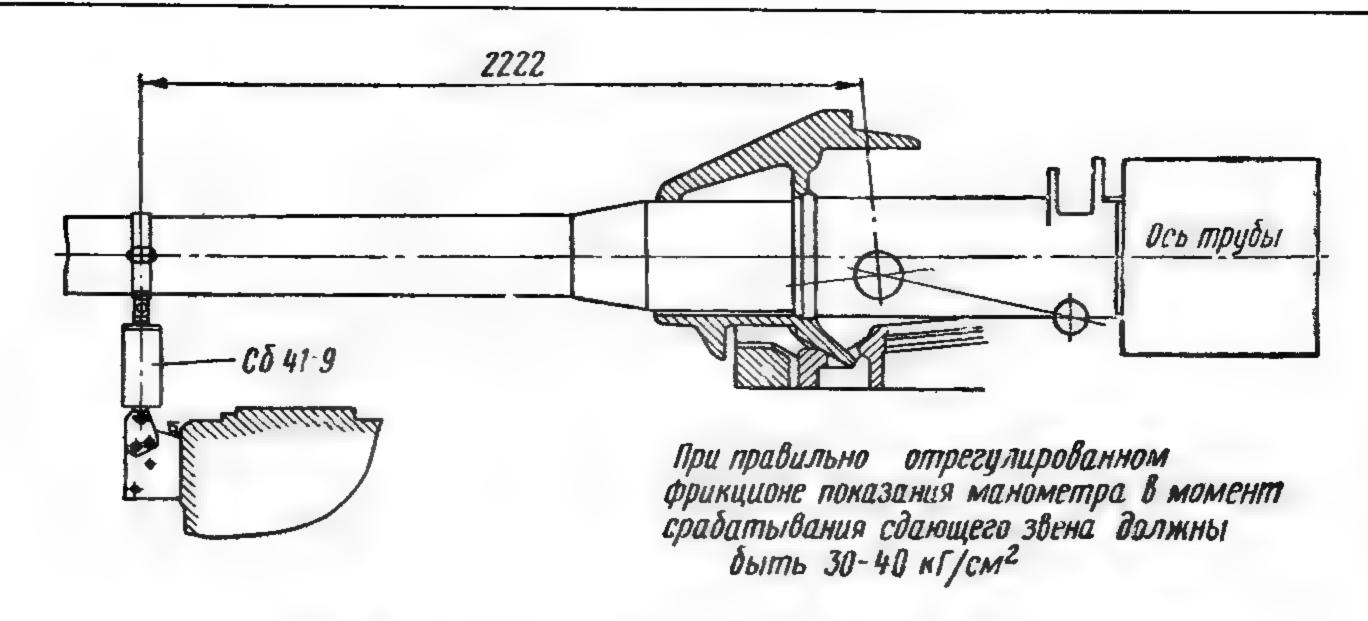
Схема установки прибора (Сб. 41-9) для проверки сдающего звена подъемного механизма
